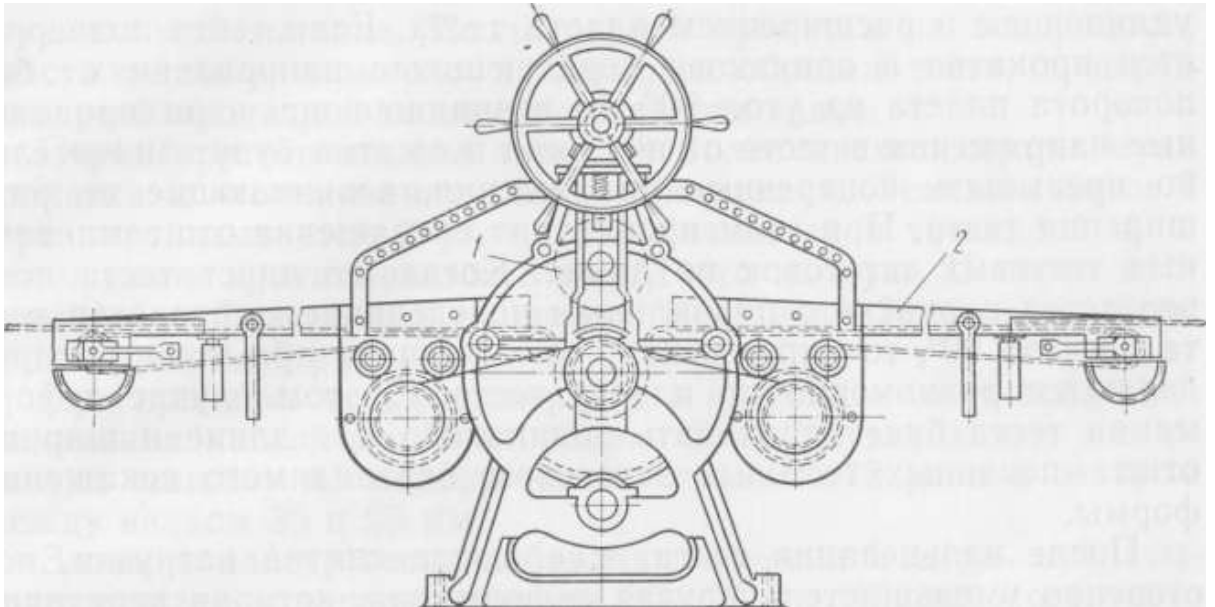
Двовалкова реверсивна машина для прокатки тіста: 1 — валки; 2 — транспортер
